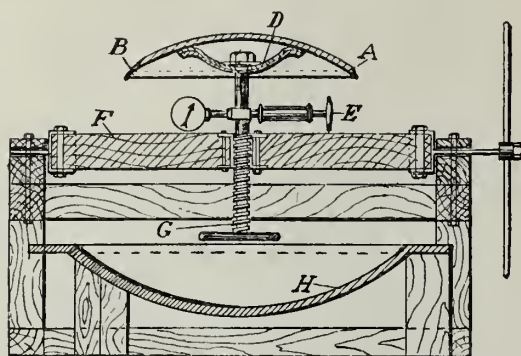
Dispositif pour l'argenture du moule destiné à la fabrication d'un miroir électrolytique.
